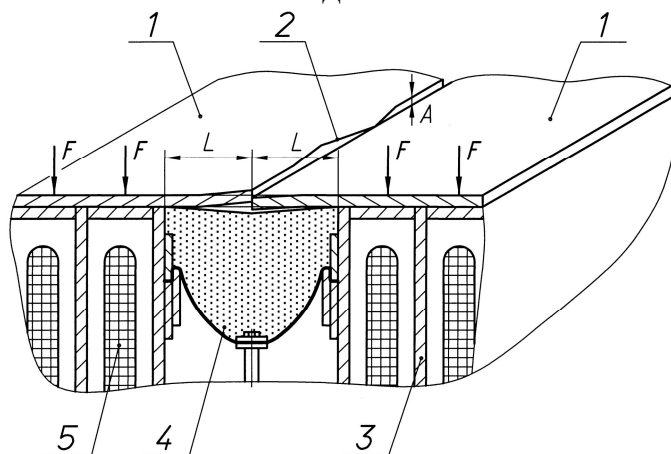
Схема сборки сварного стыка листового полотнища на электромагнитном станде с флюсовыми подушками
